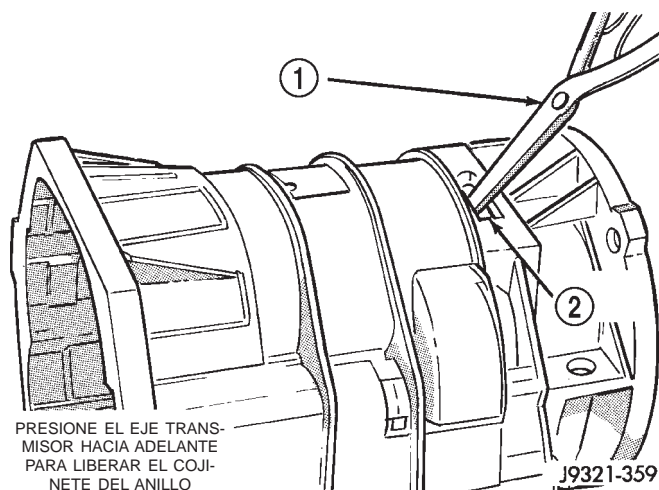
Asiento del anillo de posición en el cojinete trasero
